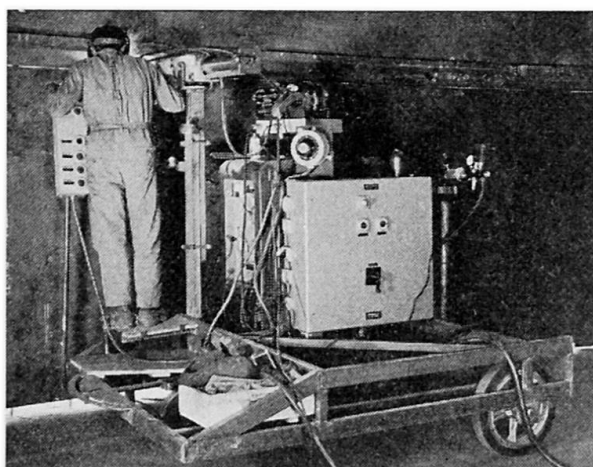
Vollautomatisches Schweißen einer Horizontalnaht.
